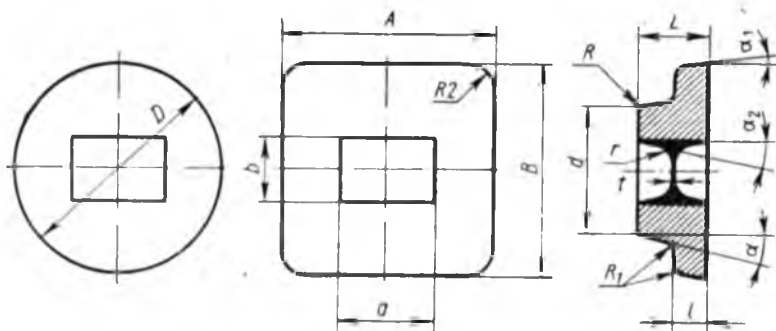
Заготовка дроссельного фланца к табл. 1.21
